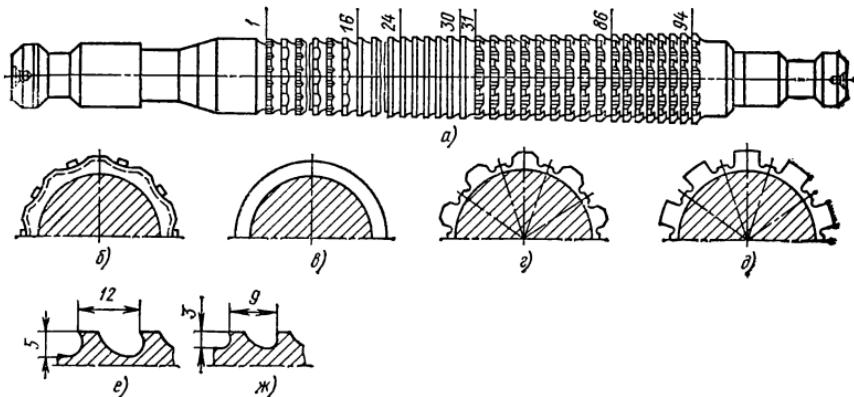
Шлицевая протяжка с переменной схемой резания (однопроходная):
